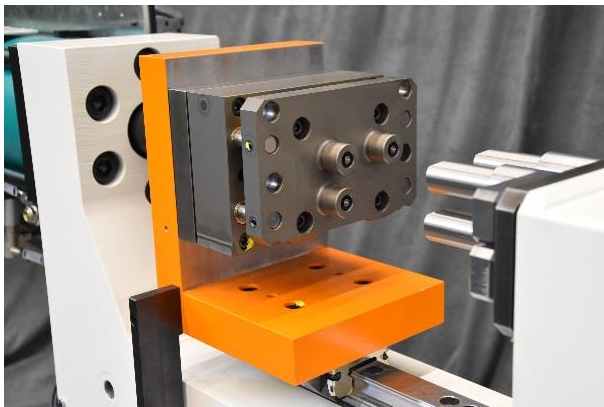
zeigt stempelseitig das Dreifach-Werkzeugsystem
